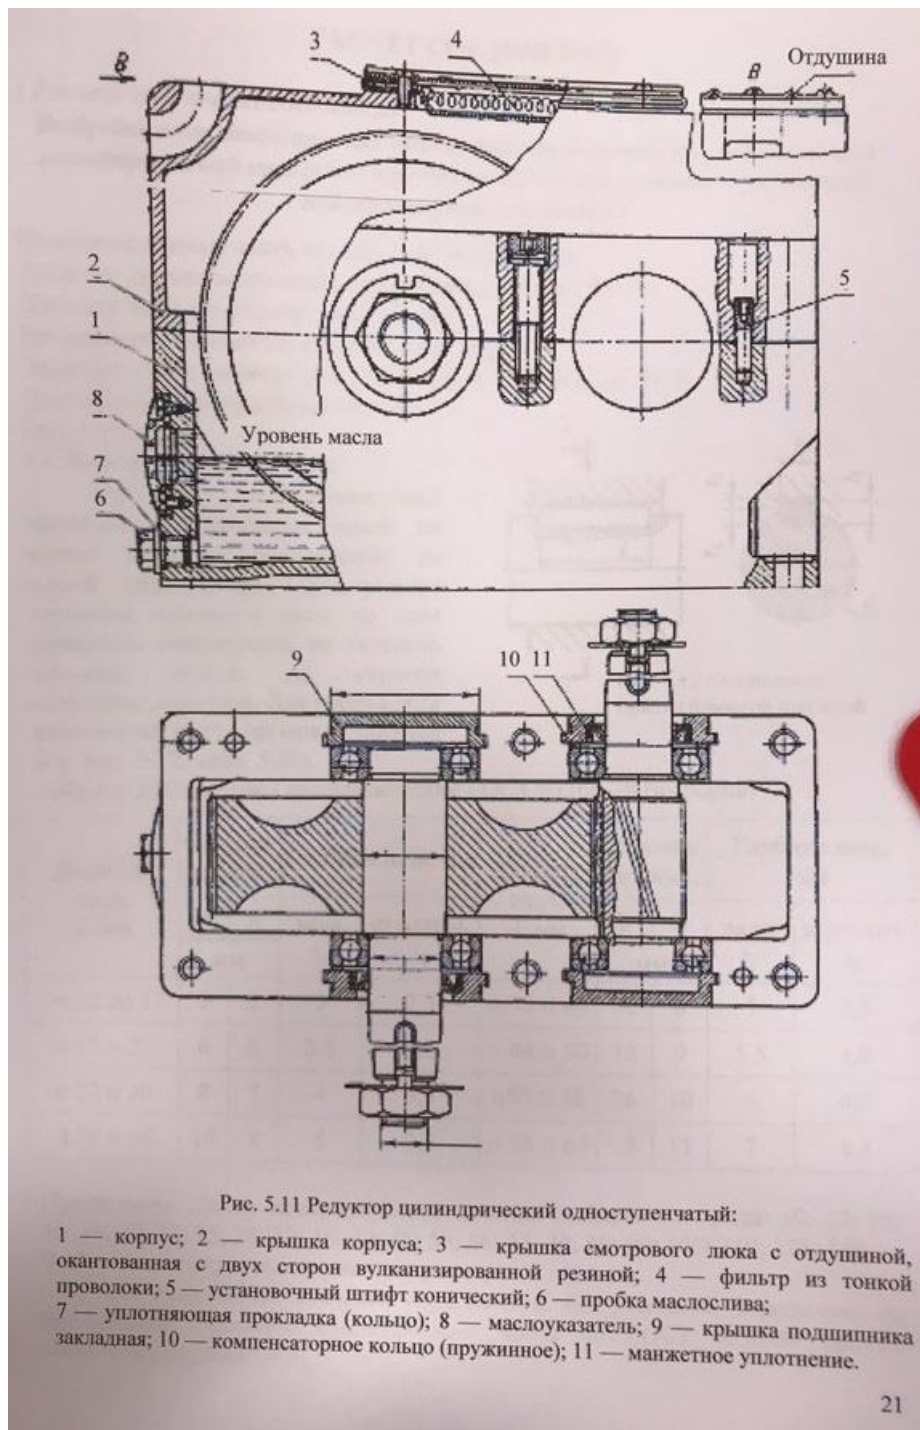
Редуктор цилиндрический одноступенчатый:
